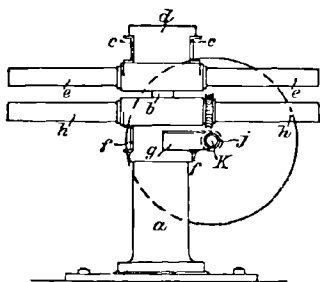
Machine à merceriser de Thomas et Prévost; vue latérale.
